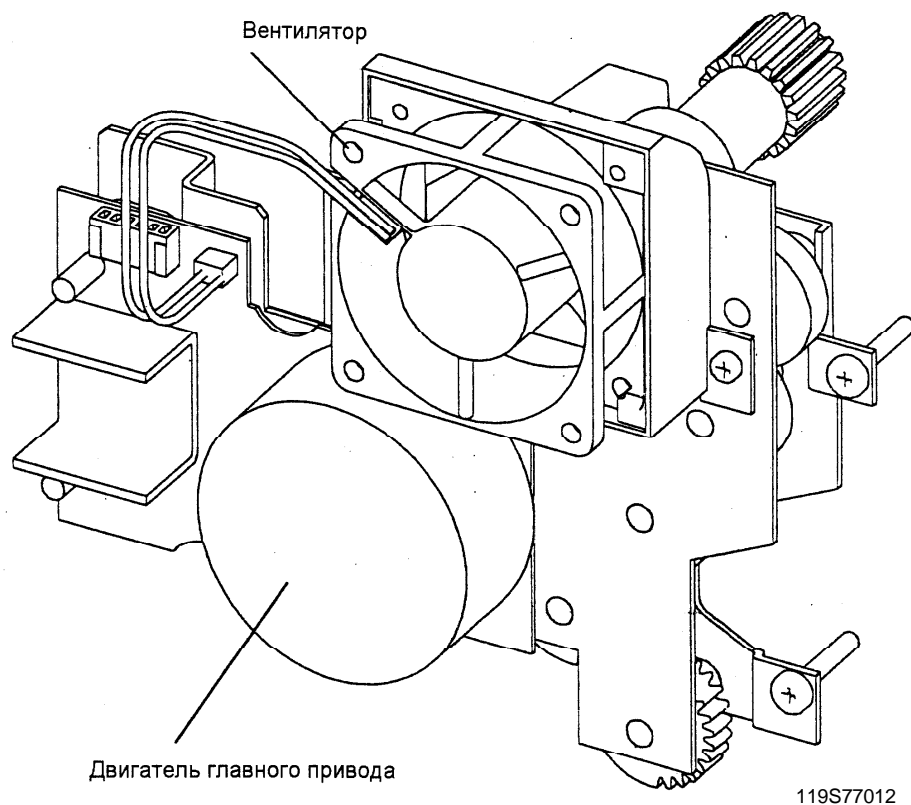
Двигатель главного привода и вентилятор охлаждения
